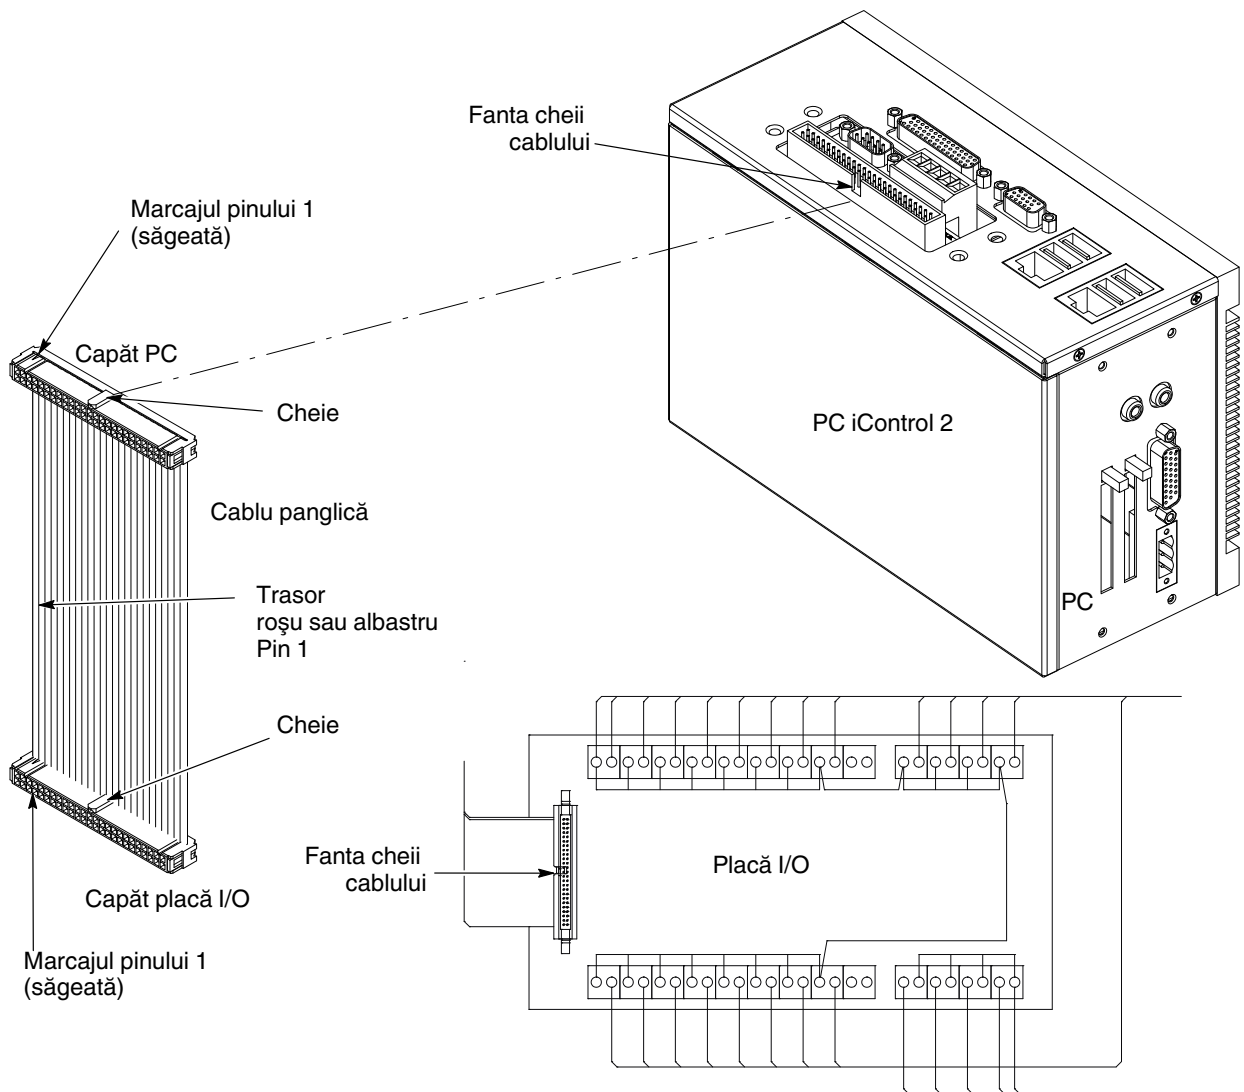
Conexiunile cablului panglică al plăcii I/O PC
